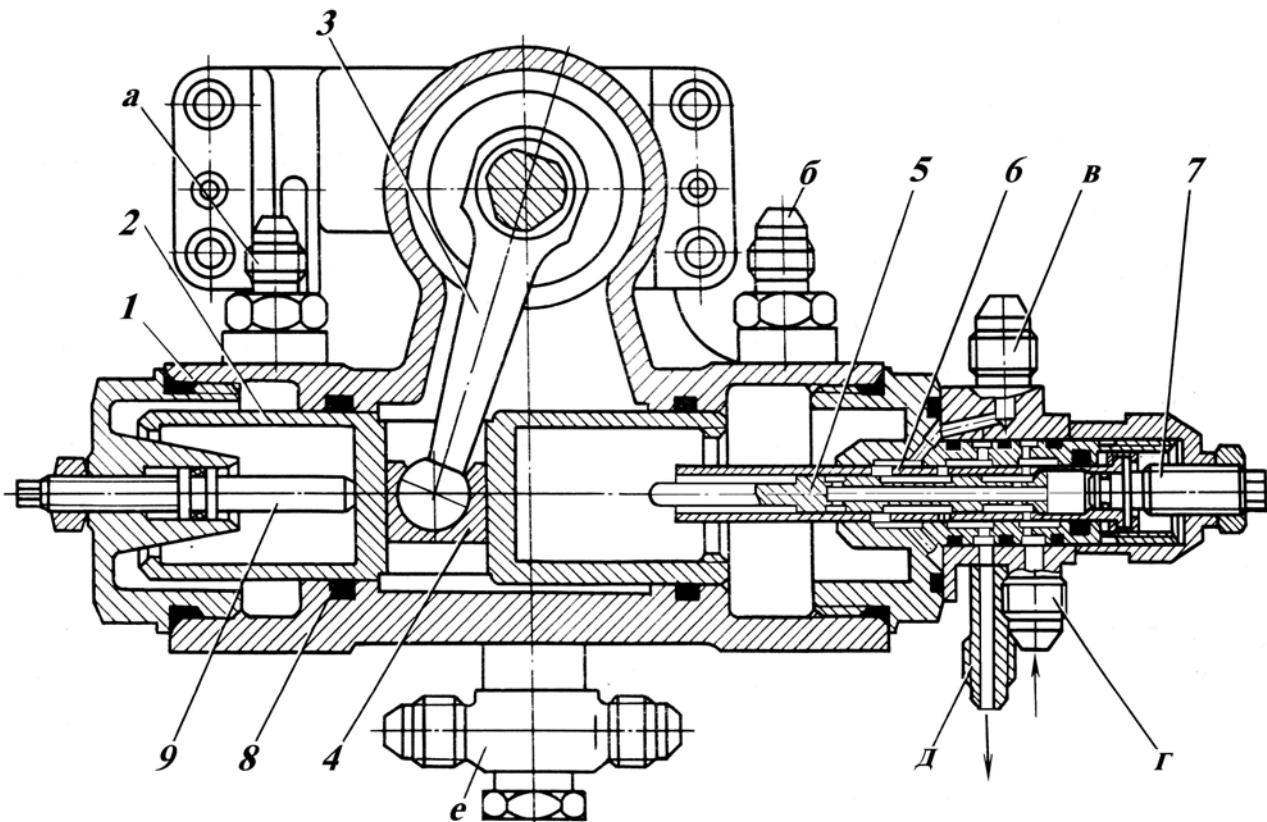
Нижний гидроцилиндр с концевым переключателем
